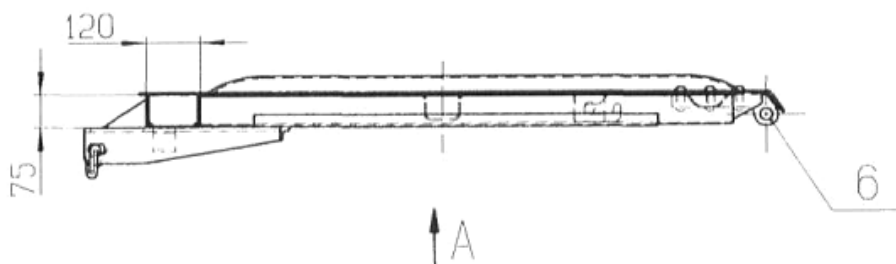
Загальний вид (вид збоку) кришки люка універсального напіввагона в робочому положенні
